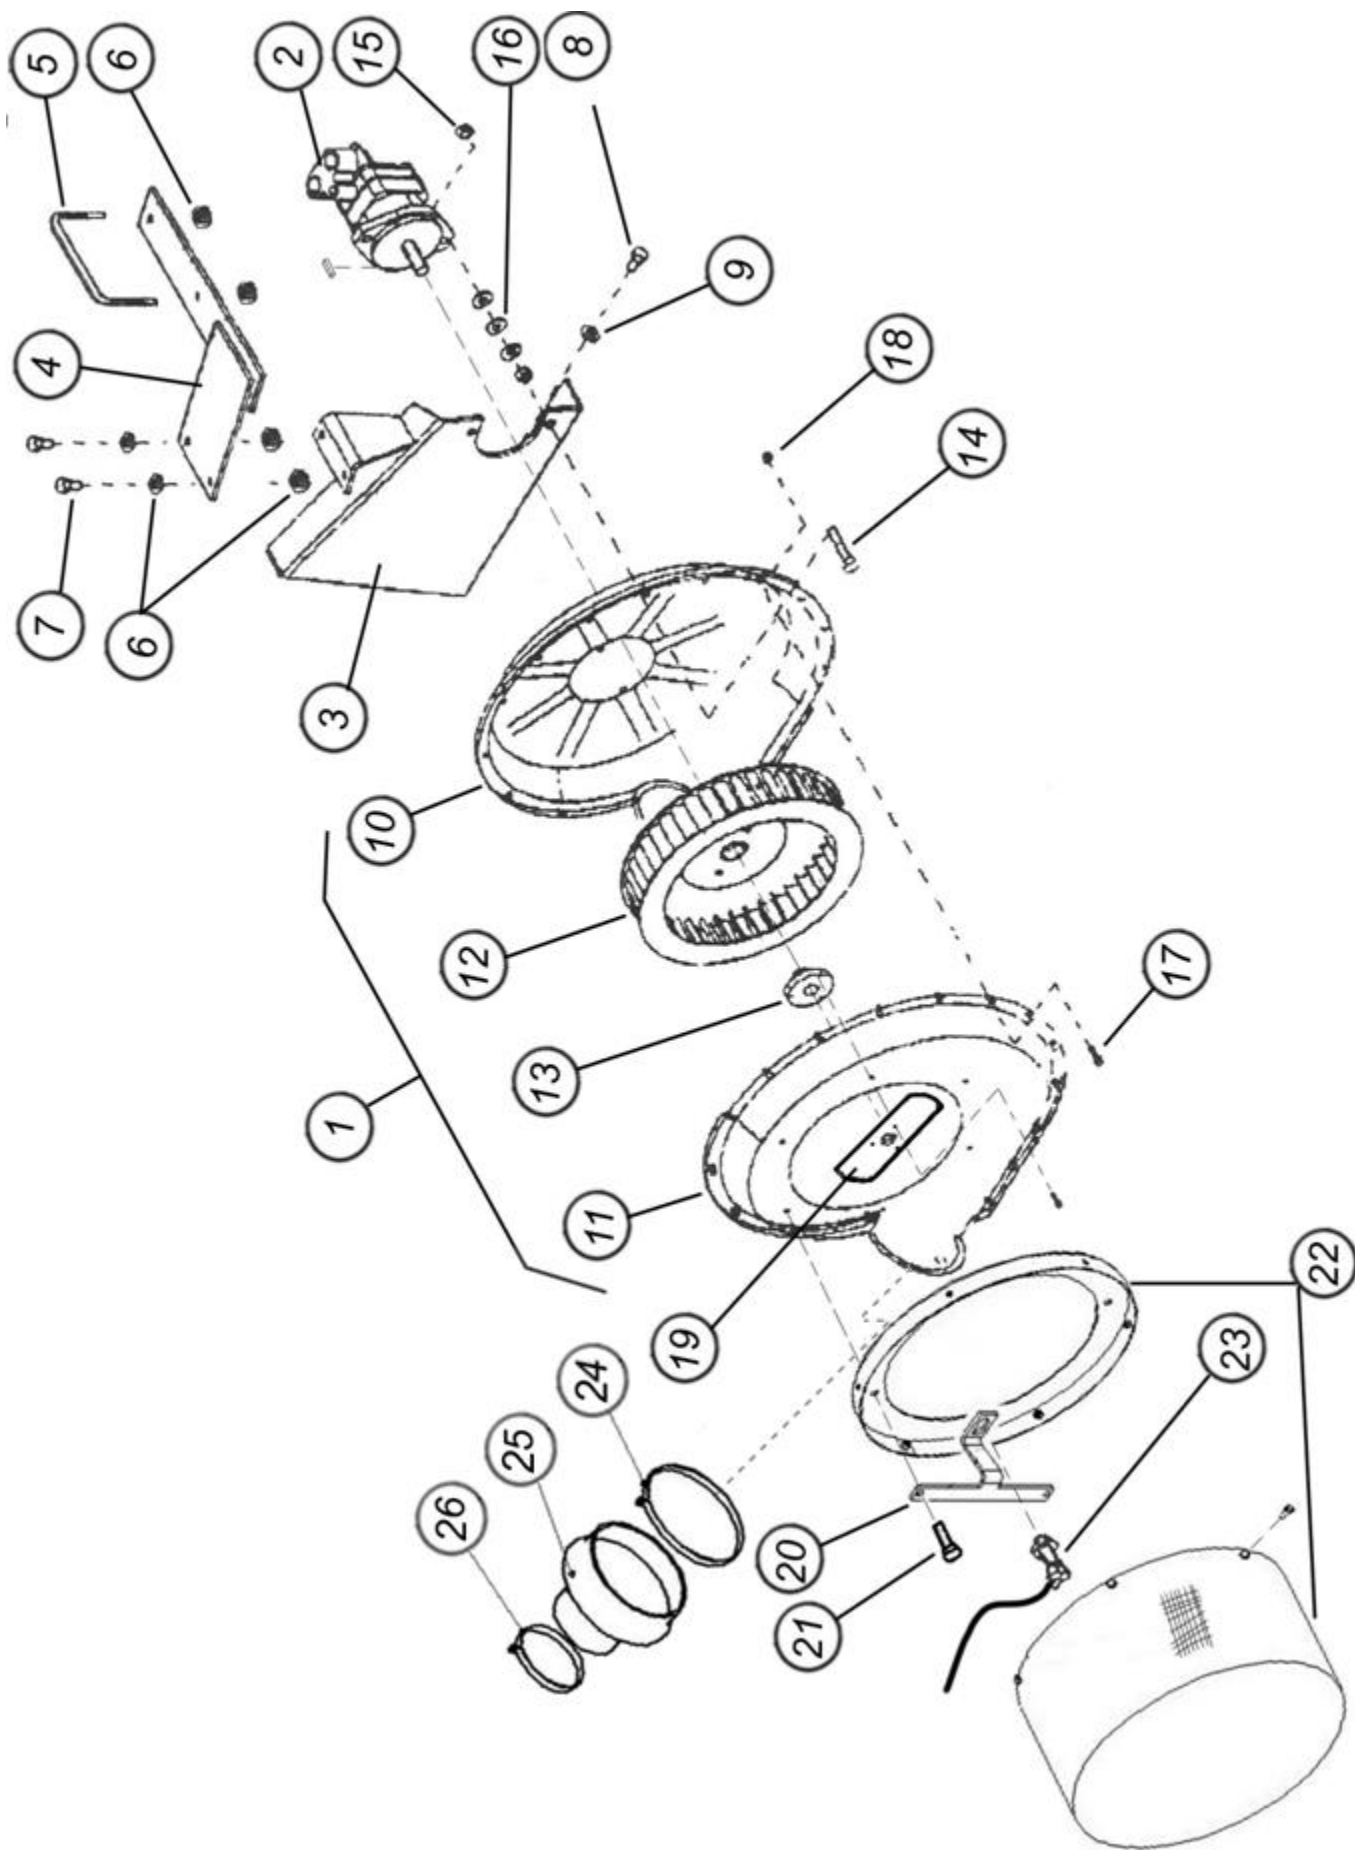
Детали и узлы вентилятора 6" с гидроприводом
